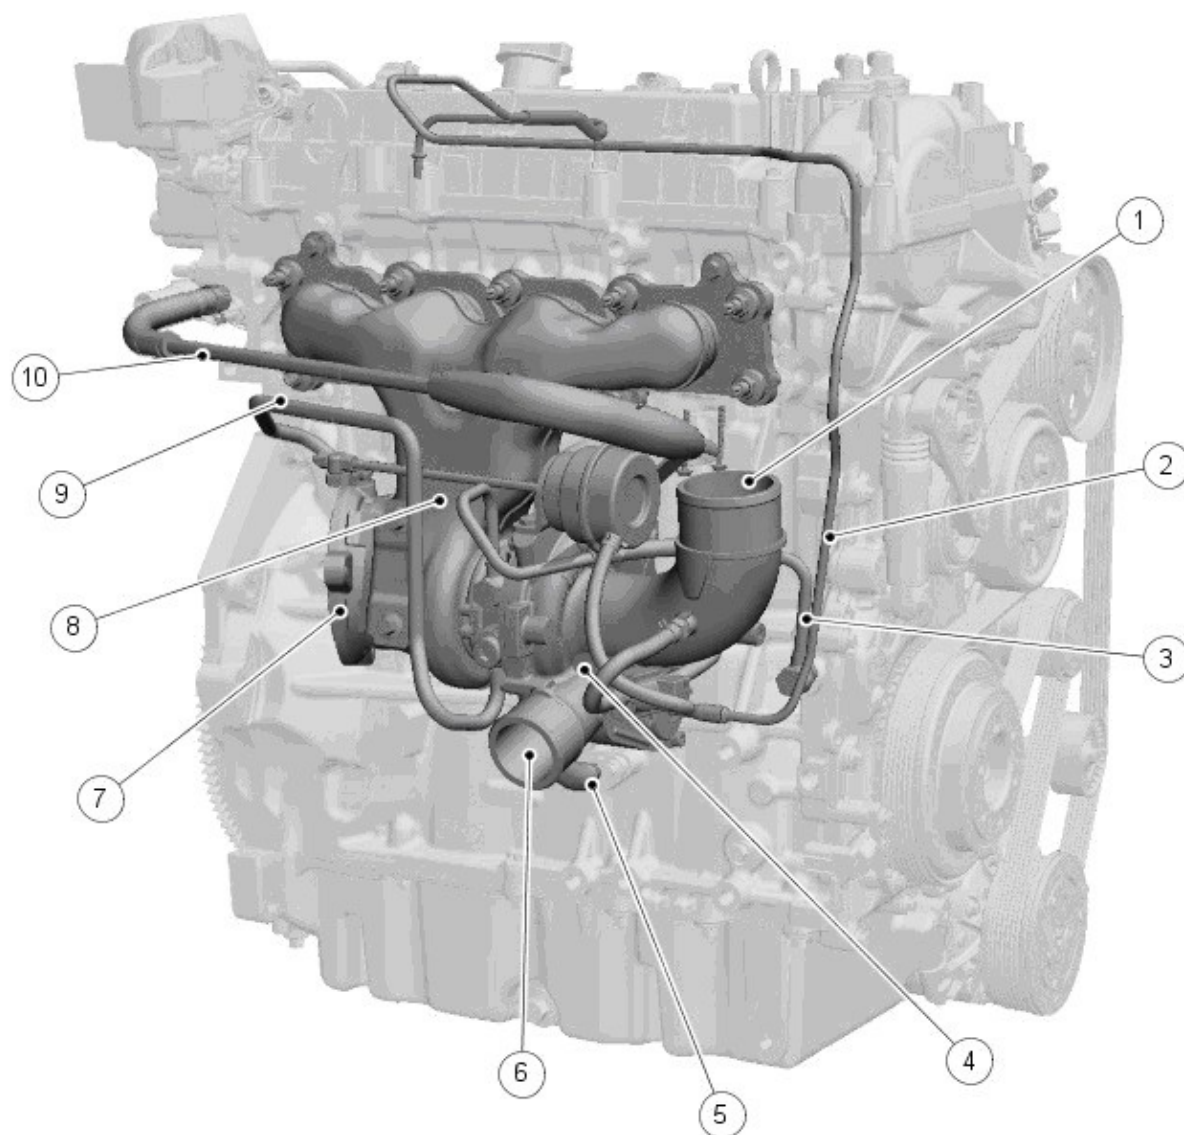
Расположение компонентов турбокомпрессора бензинового двигателя 2.0L GTDi
